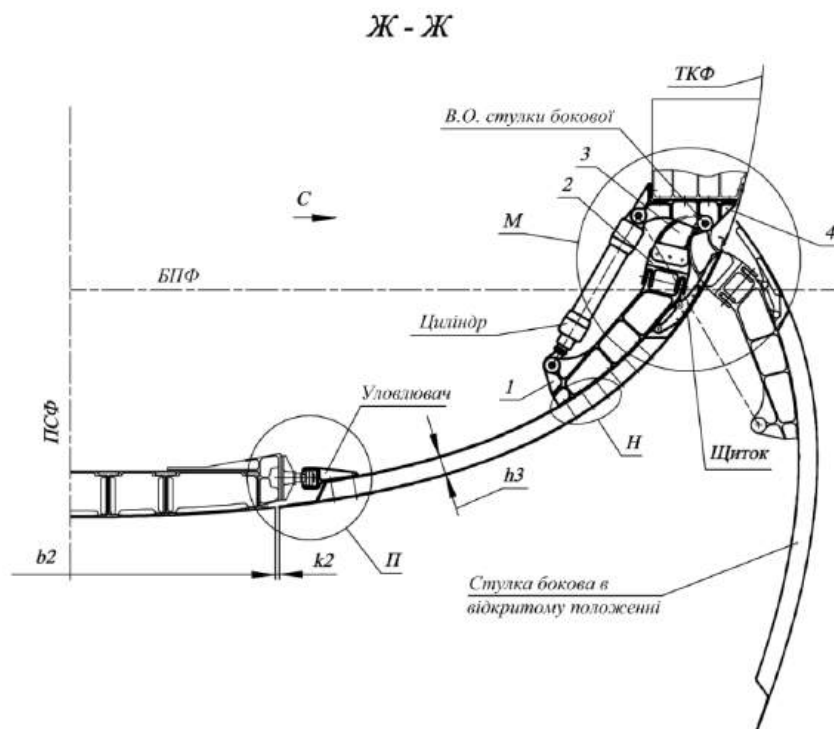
Схема установки циліндрів керування бічними стулками
